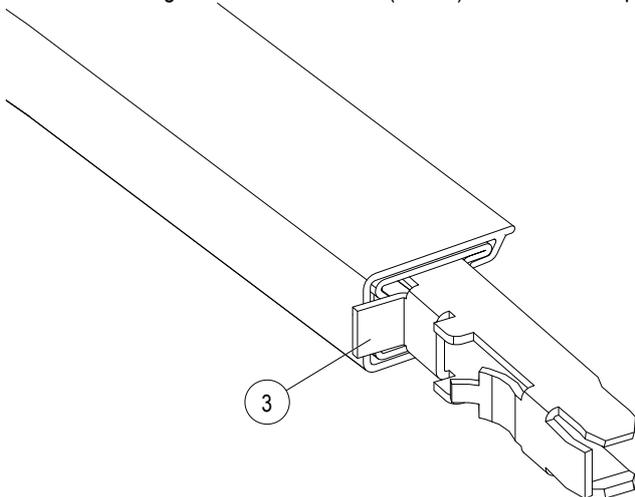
Der Anschlag (Pos. 3) des Steckverbinders liegt am Isolierprofil an
